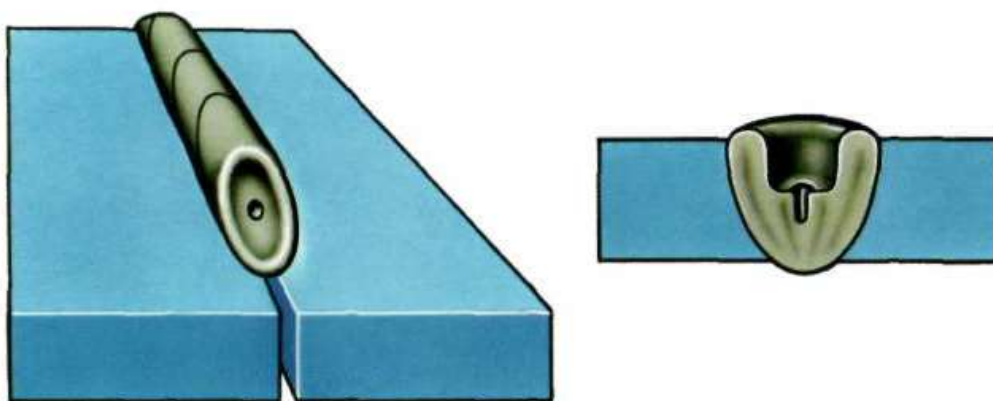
Дефект сварного шва по типу кратера
